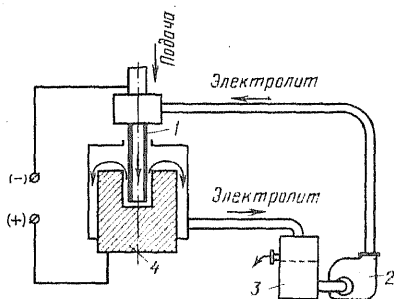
Схема установки для глубокой электрохимической обработки металлов:
